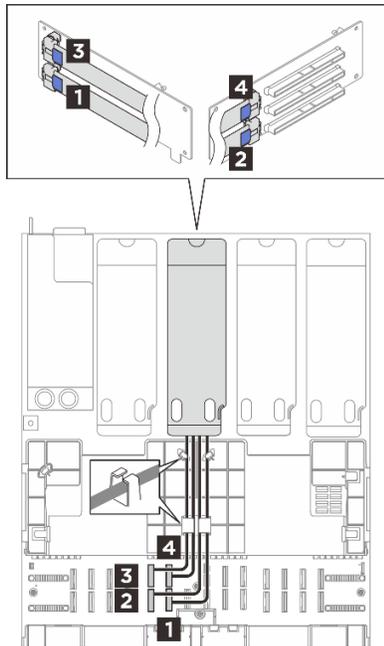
Kabelführung für PCIe-Adapterkarte C
